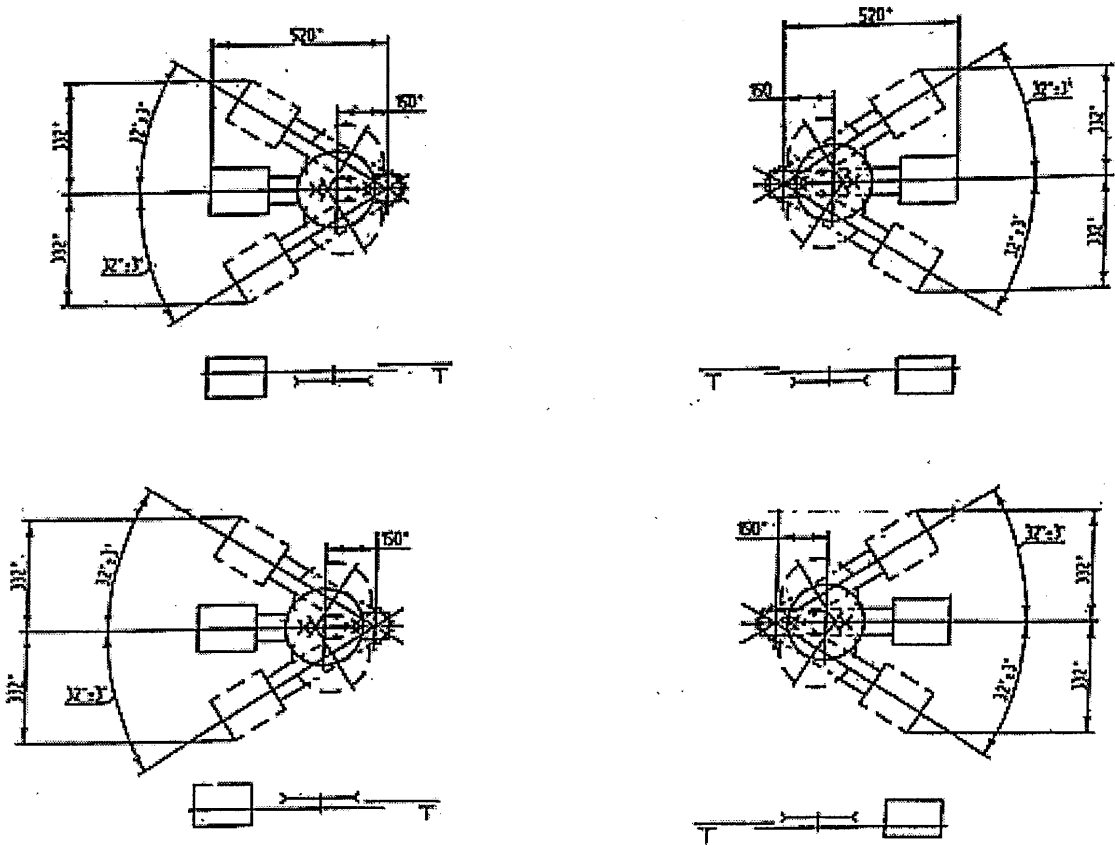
схемы сборки натяжного устройства каната ОС
